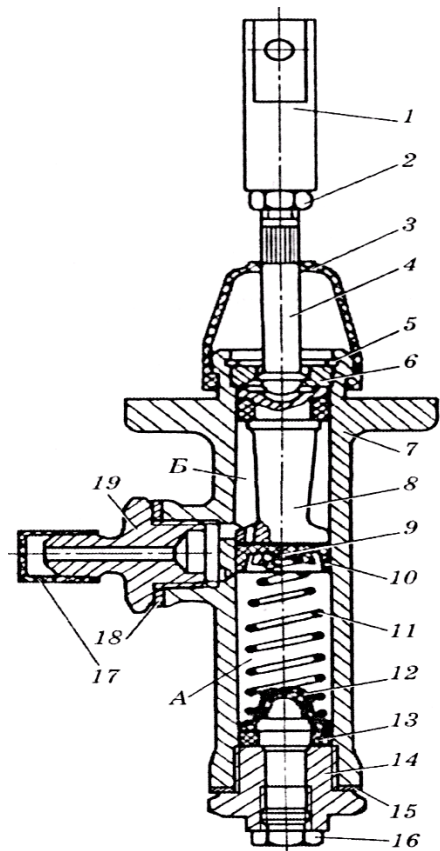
Головний гідроциліндр: 1 – вилка; 2 – гайка; 3 – чохол; 4 – штовхач; 5 – стопорне кільце; 6 – упор; 7 – корпус; 8 – поршень; 9 – перепускний клапан; 10 – манжета; 11 – пружина; 12 – клапан; 13 – упорне кільце; 14, 19 – штуцери; 15, 18 – ущільнювальні прокладки; 16, 17 – пробки транспортні, *A*, *B* – порожнини
